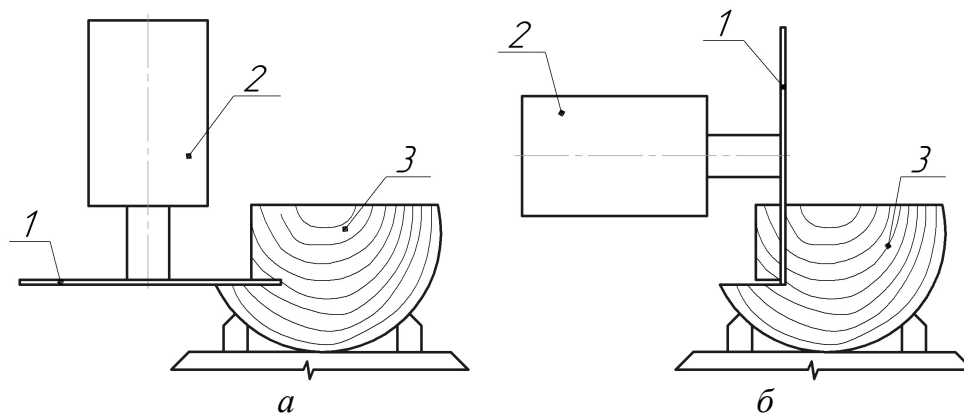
Цикл розпилювання колоди на ортогональному верстаті з поворотною круглою пилкою: а – прямий робочий хід; б – зворотний робочий хід;
